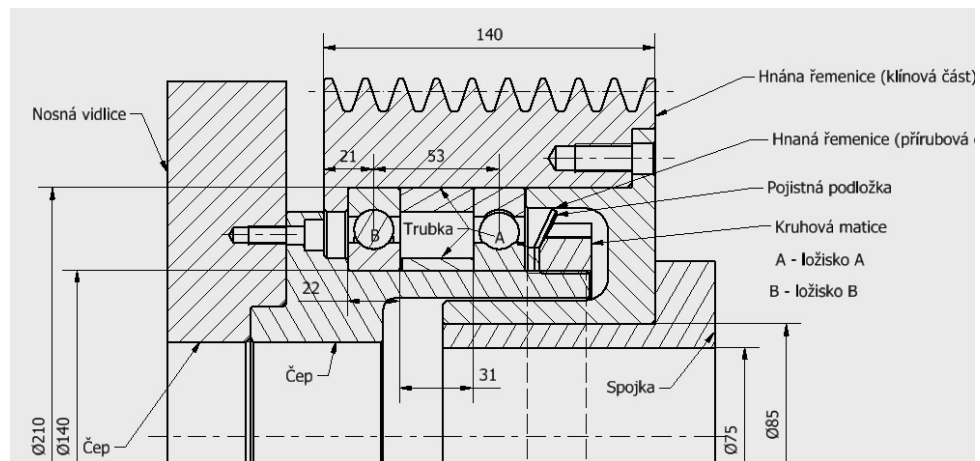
Spojka ETP-TECHNO a princip její činnosti [14]:
